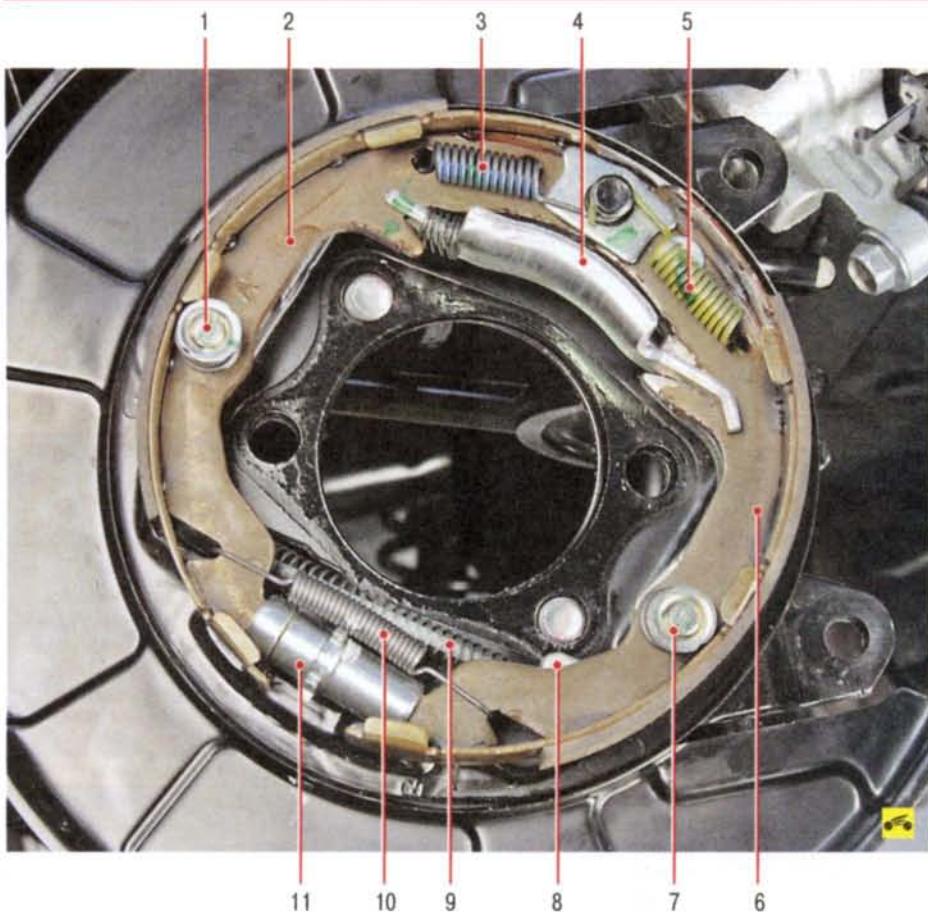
Детали стояночного тормозного механизма: 1, 7 – опорные стойки колодок; 2 – передний колодка стояночного тормоза; 3 – верхняя стяжная пружина передней колодки; 4 – разжимная планка; 5 – верхняя стяжная пружина задней колодки; 6 – задняя колодка стояночного тормоза; 8 – разжимной рычаг привода колодок; 9 – задний трос стояночного тормоза; 10 – нижняя стяжная пружина колодок; 11 – регулировочное устройство тормозных колодок стояночного тормоза
